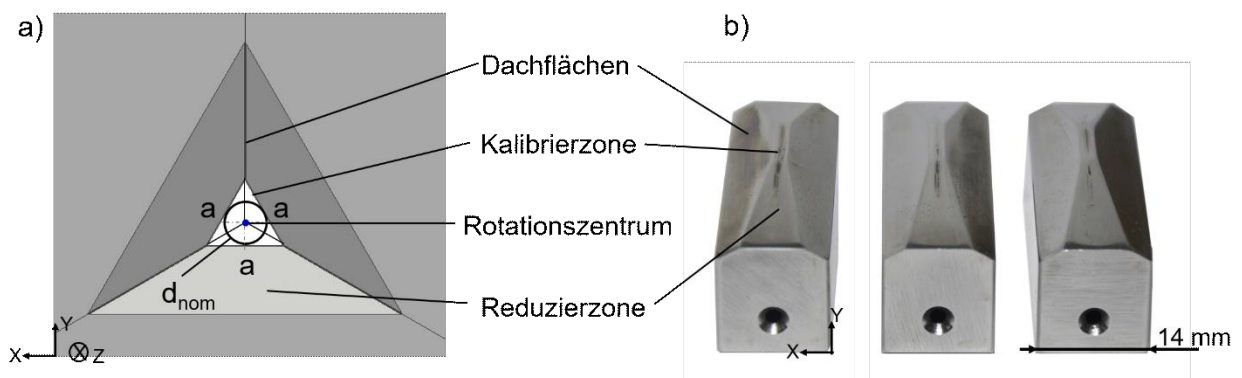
Werkzeugkonzept Doppelflachwerkzeuge: a) Bildung eines gleichseitigen Dreiecks durch drei Flächen der DFW in der Kalibrierzone; b) Werkzeugsatz bestehend aus drei Doppelflachwerkzeugen.
